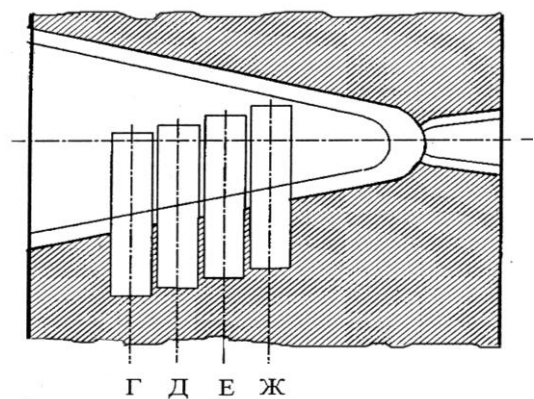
Схема вирізки заготовок ЗС типу "Ш" і "С" з металу ЗТВ.
